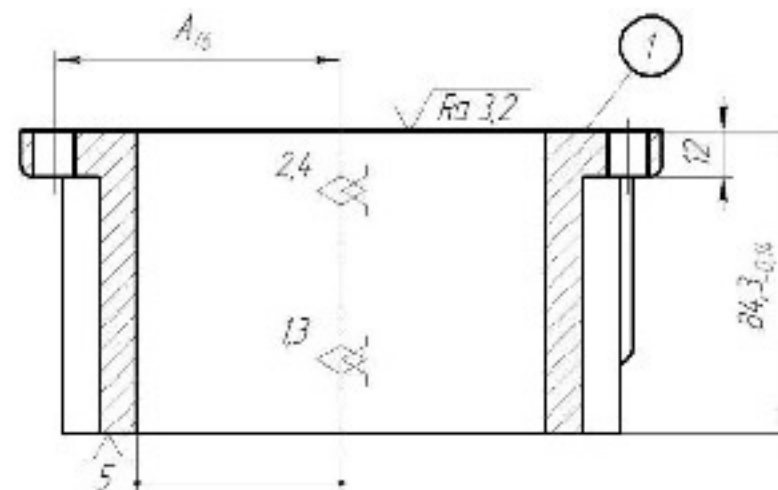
Ескіз і схема базування на 005 операції при обробці чистових баз
